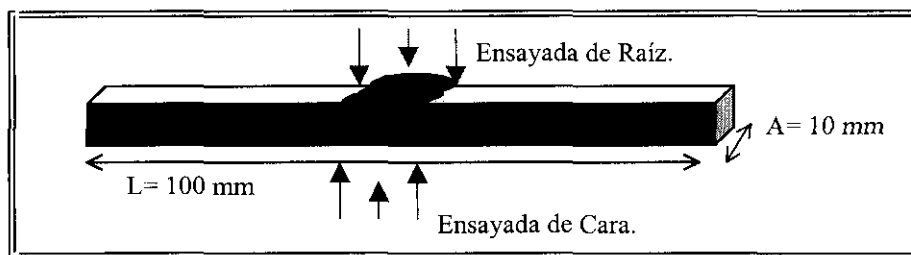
Probeta de Doblado en probetas soldadas.
